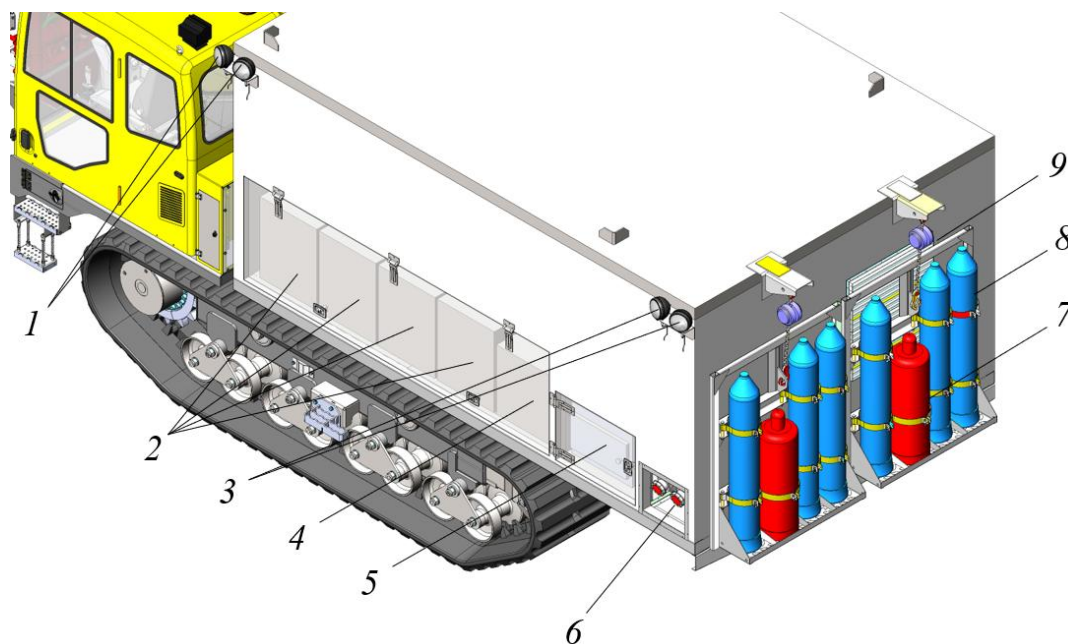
Агрегат гусеничный сварочный
